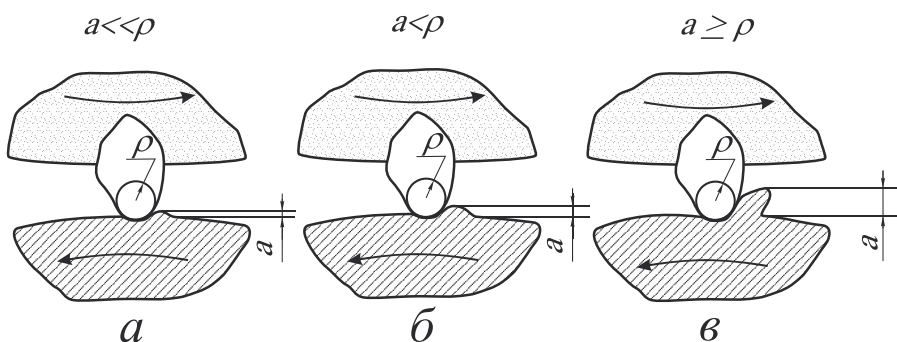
Схема зняття стружки алмазним зерном з металічної поверхні
